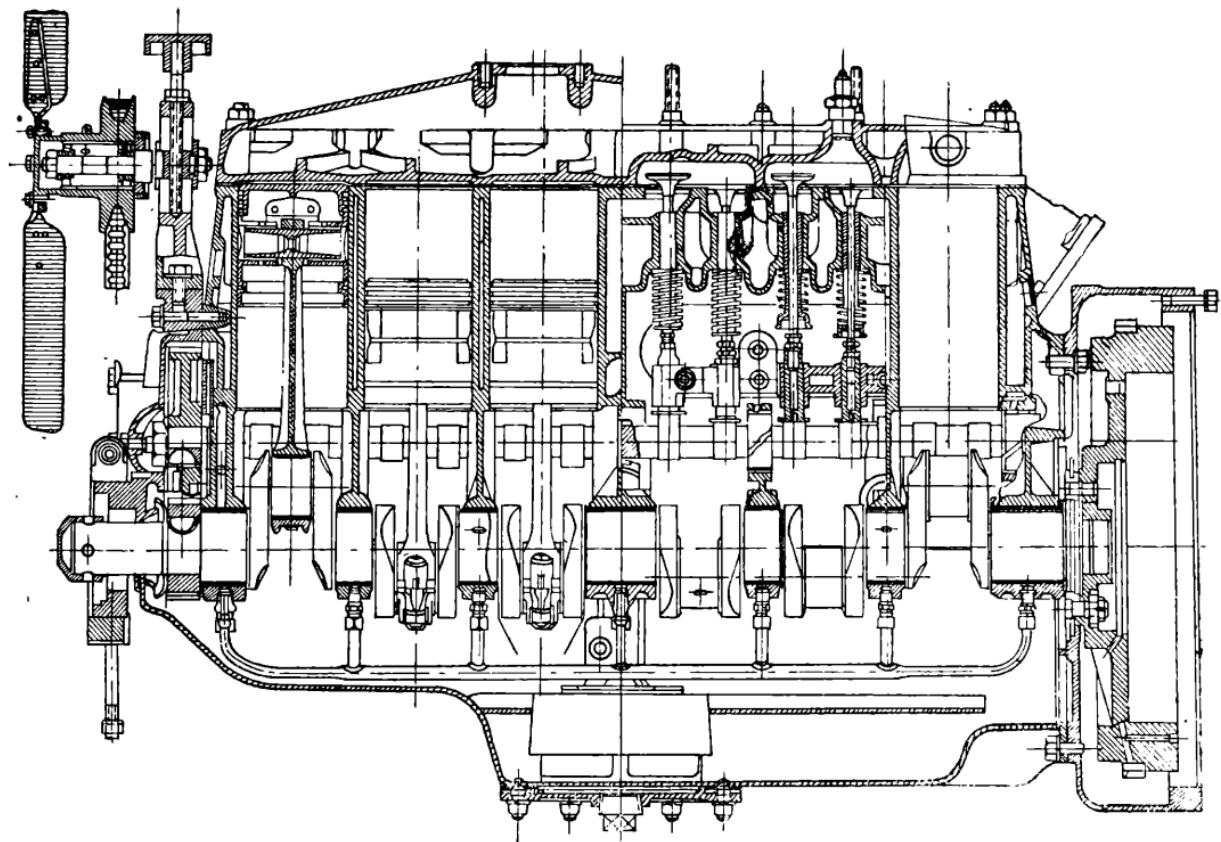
Двигатель ЗИС. Вид со стороны распределителя.
